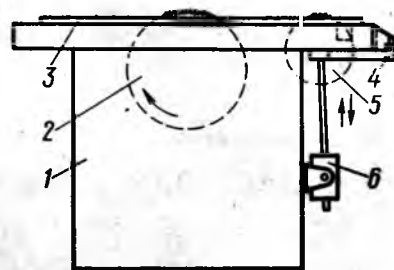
Схема модернизированного станка Ц6 с механизмом управления подрезающей пилой
